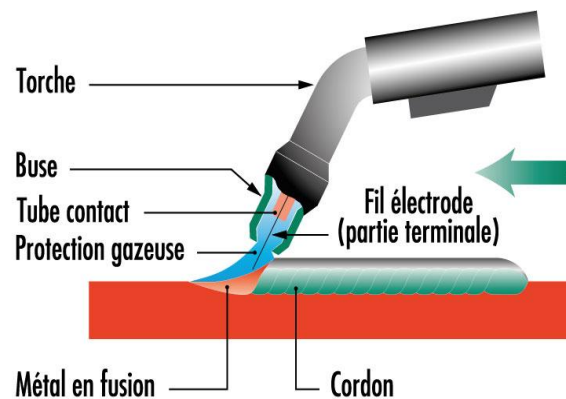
La torche MIG et son procédé de soudage.
